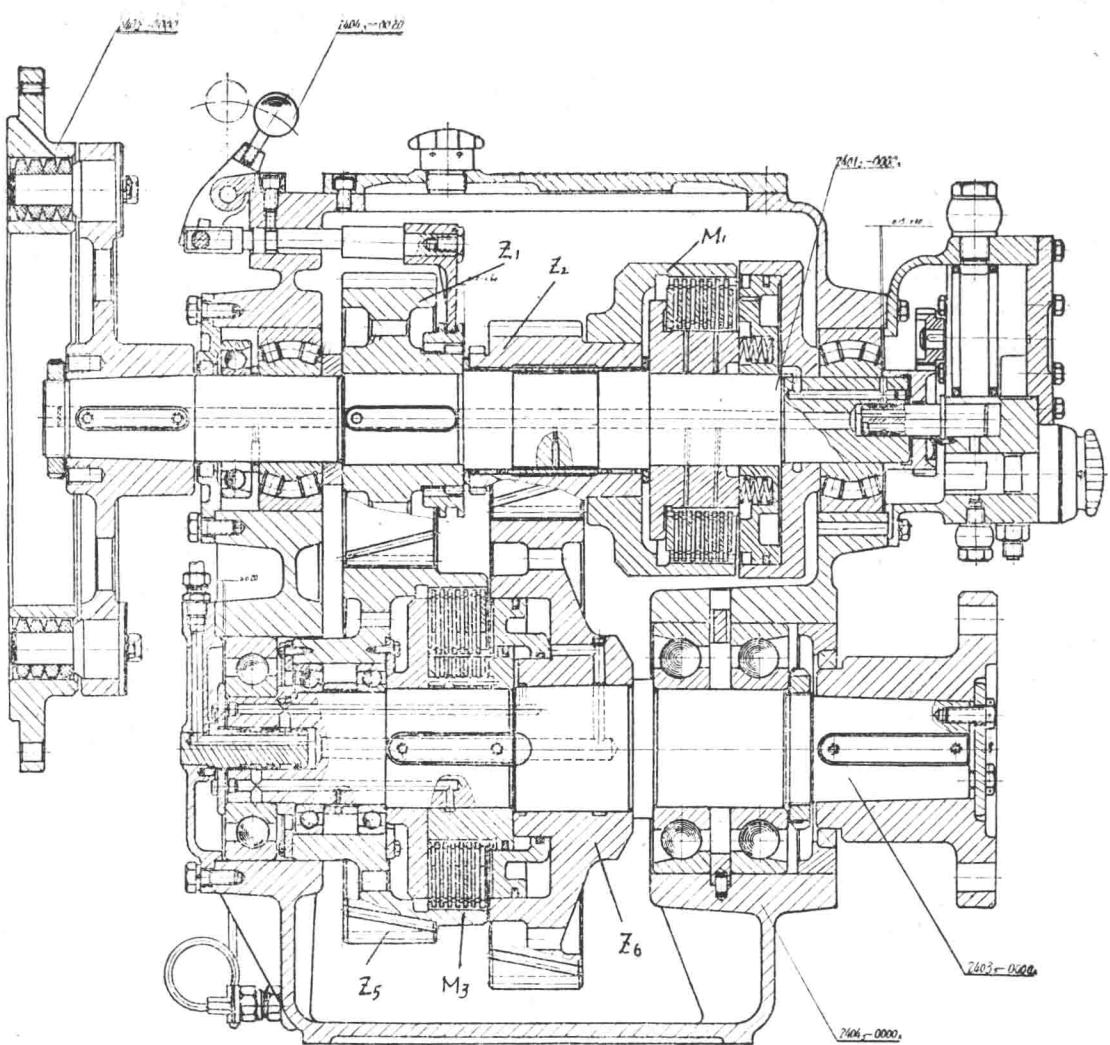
杭州齿轮箱厂 ZF240 双速倒顺车齿轮箱
